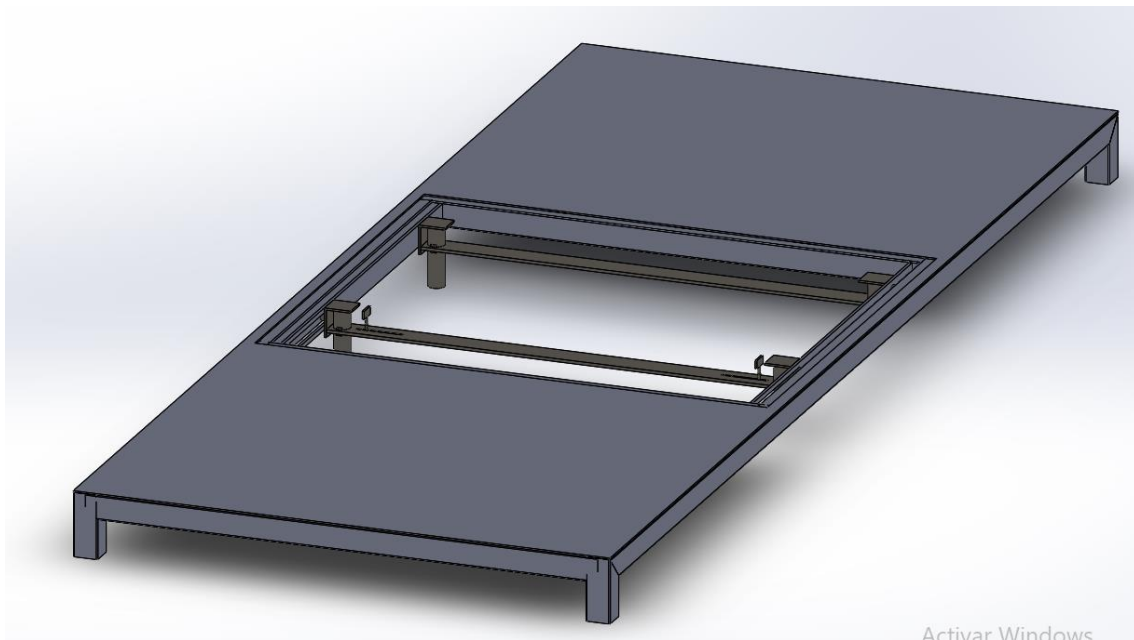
Estructura cubierta con plancha de 2 mm de espesor.
